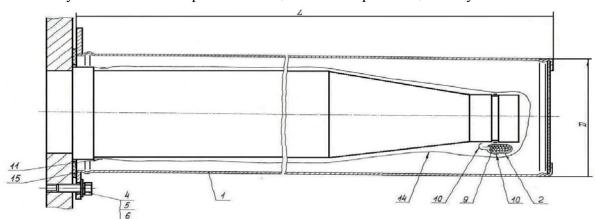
установка транспортировочного корпуса на нижнюю часть RIP-изоляции 1 — транспортировочный корпус; 2 — мешок; 3 - ; 4 — болт M 8×25.36.029: 5 — шайба A8.02; 6 — шайба 8 65 Γ .029; 9 — силикагель КСМ Γ ; 10 — Π 9-40-62-x/6; 11 — лента Π 8-40-10; 14 — полиэтиленовый пакет; 15 — прокладка резиновая.
